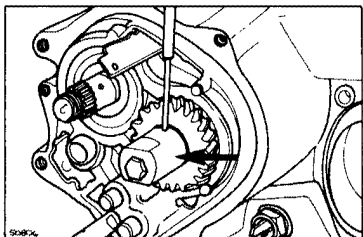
Запрессовка шестерни 5-ой передачи с помощью специального приспособления
